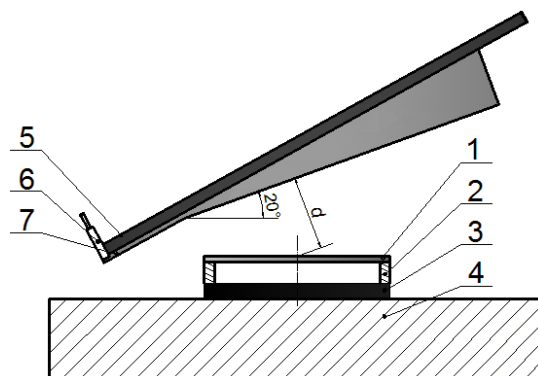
Схема сварки взрывом: 1 – пластина циркония; 2 – прокладки; 3 – пластина меди; 4 – основание; 5 – слой ПММА; 6 – детонатор; 7 – ВВ;  $d$  – расстояние от центра поверхности метаемой пластинки до ВВ (20 мм)
